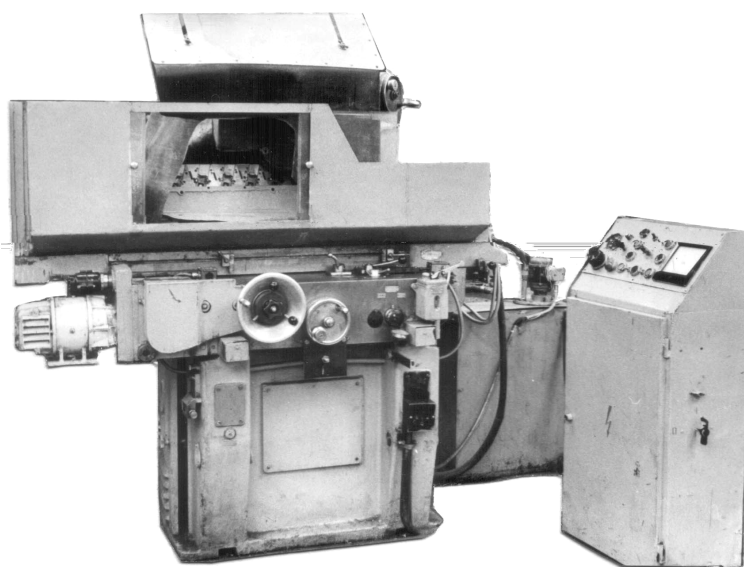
Плоско-шлифовальный станок типа 3Г-71, модернизированный для электроабразивного шлифования плоских и профильных поверхностей
